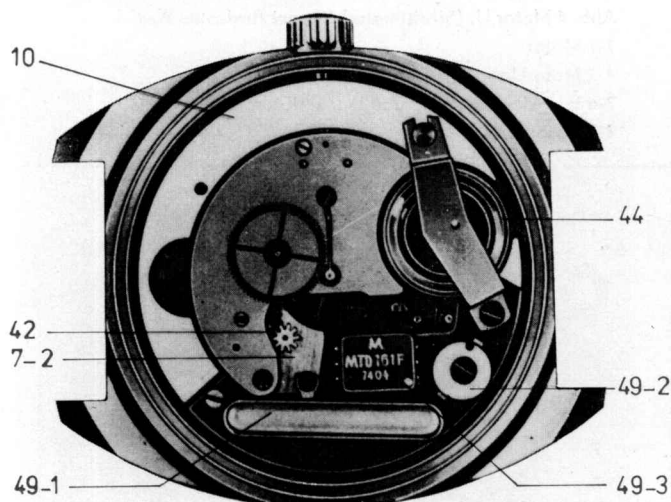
Rückansicht des Werkes 28–40 Ausf. I
